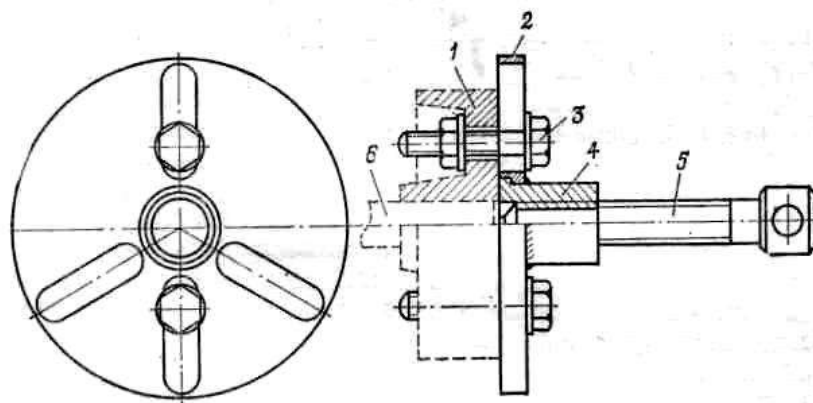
Съемник: 1 – полумуфта; 2 – диск съемника; 3 – болт; 4 – гайка; 5 – винт; 6 – вал электродвигателя
